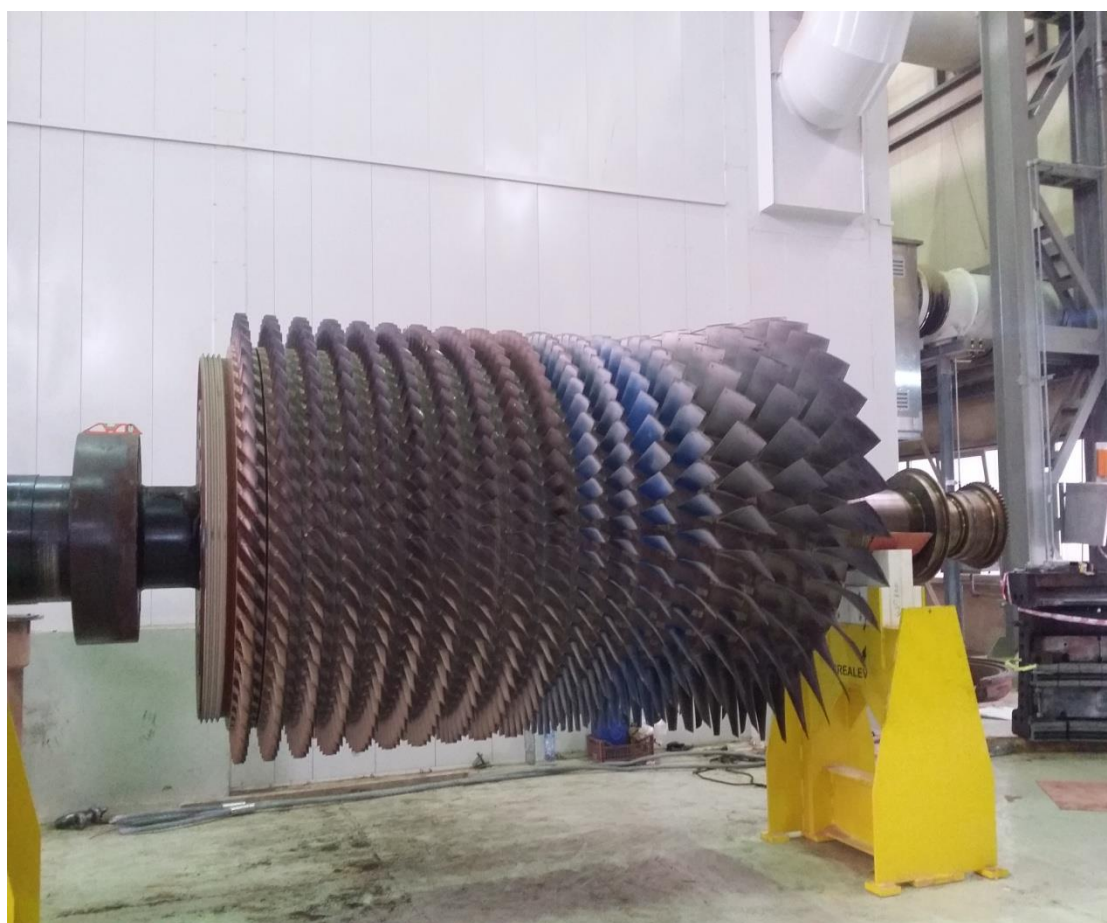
Vue réel de compresseur de turbine à gaz 9E.
